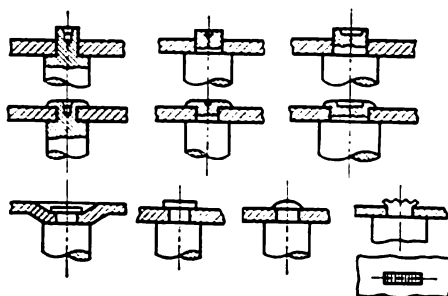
Assemblage de pièces tôlées avec des pièces cylindriques
